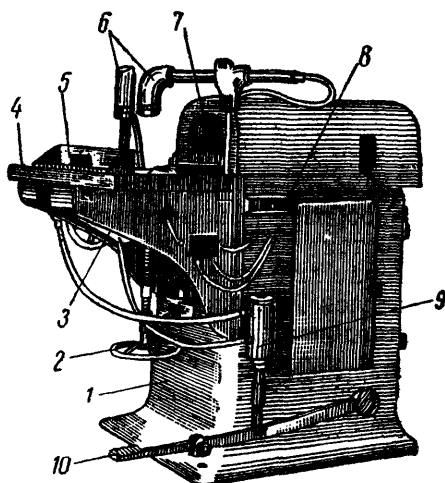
Сверлильно-пазовальный станок СвПА с автоматической подачей.
